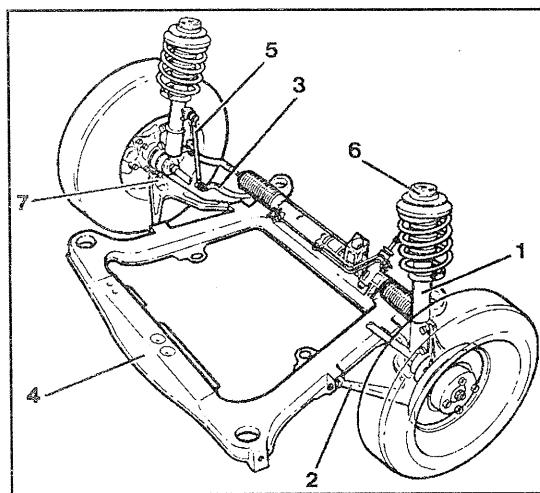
(1 — амортизационная стойка; 2 — шарнирный рычаг; 3 — стабилизатор поперечной устойчивости; 4 — вспомогательная рама; 5 — шарнир; 6 — верхнее кольцо; 7 — шаровой шарнир).
